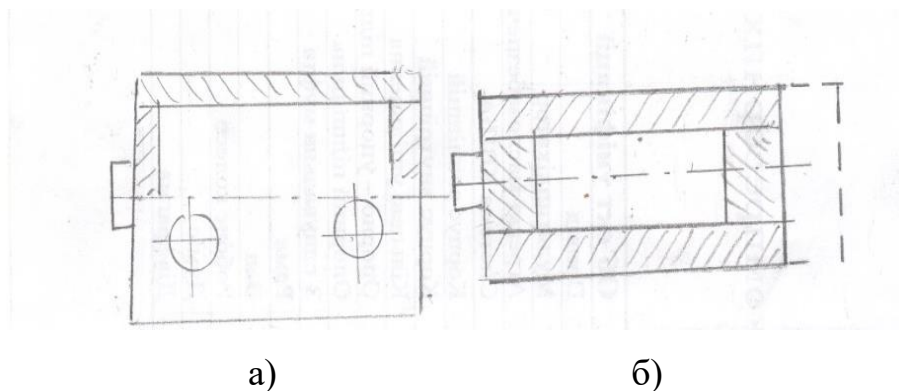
Корпуса з вертикальним роз'ємом (схеми)
